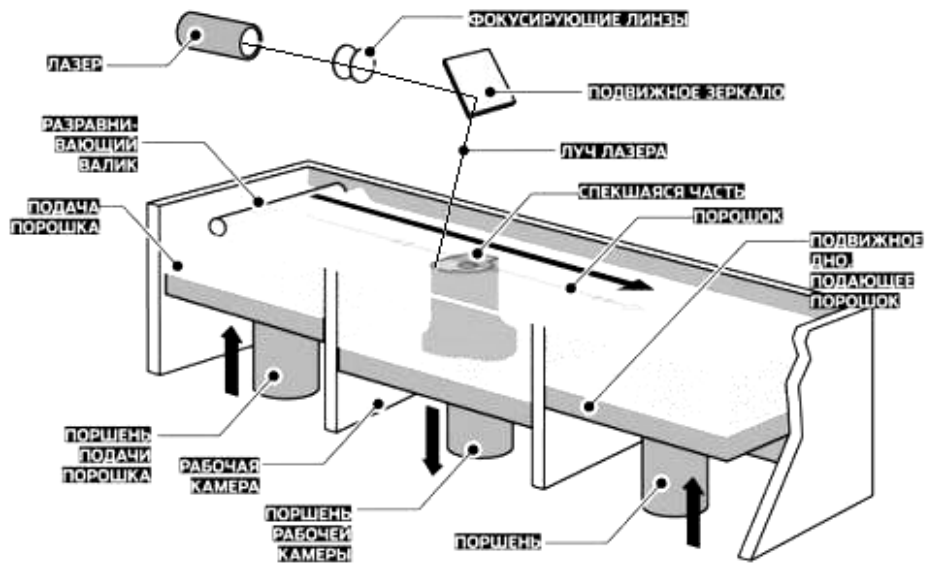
Схема установки для лазерного спекания порошков с порошковой камерой
